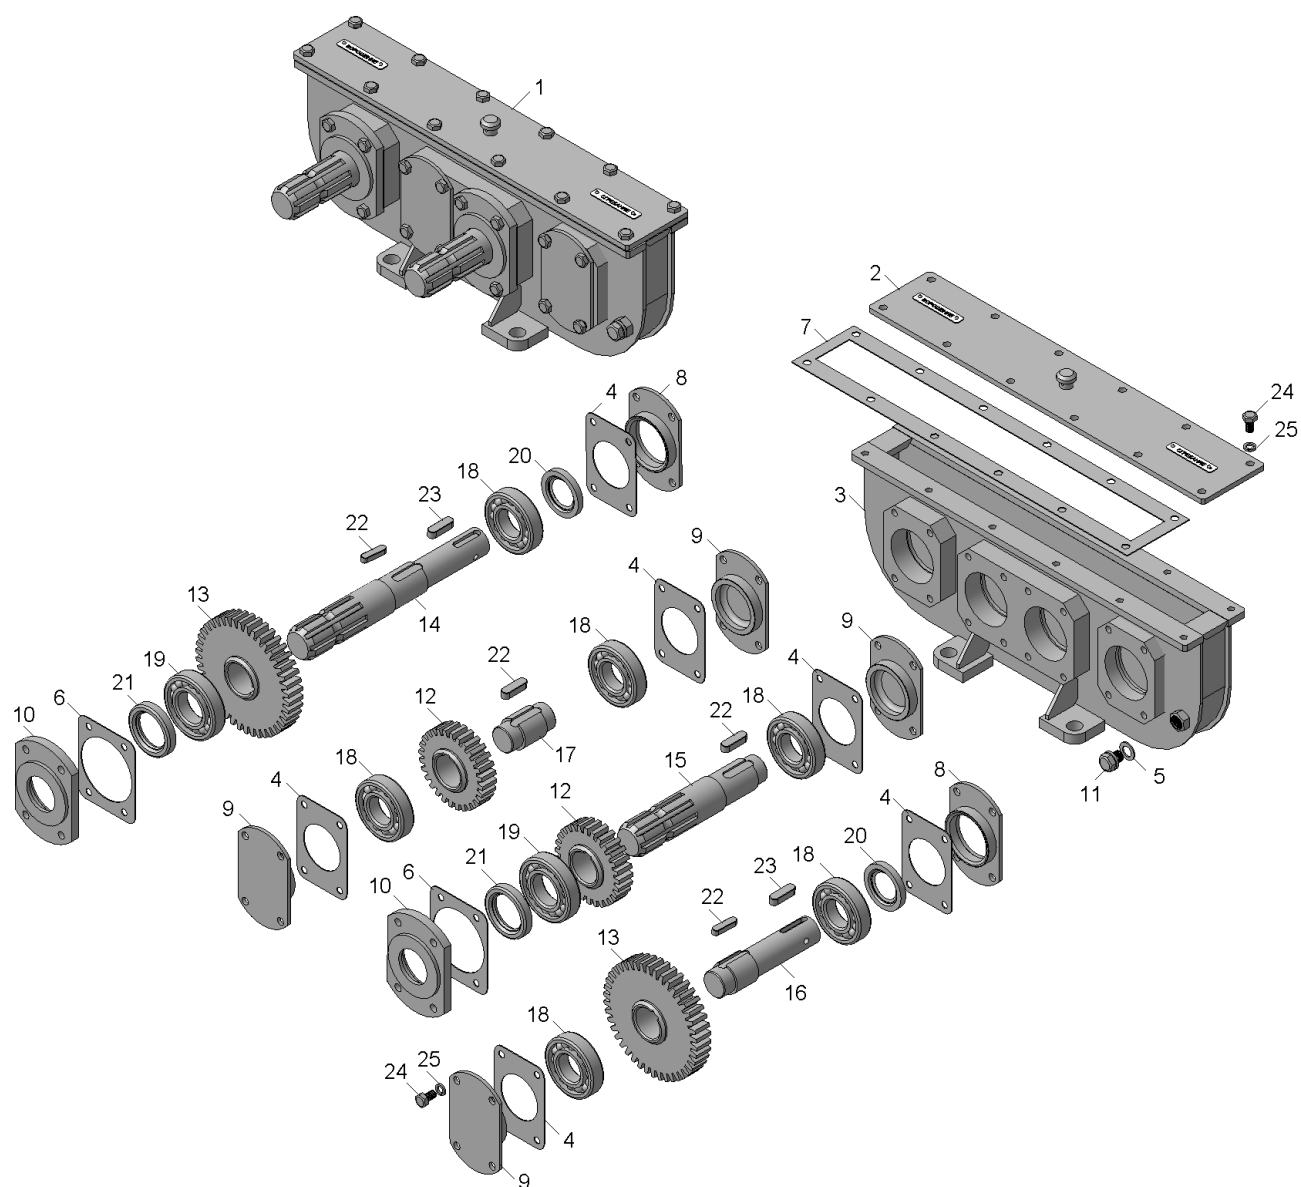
Редуктор УГМ-4,2.04.00.000
